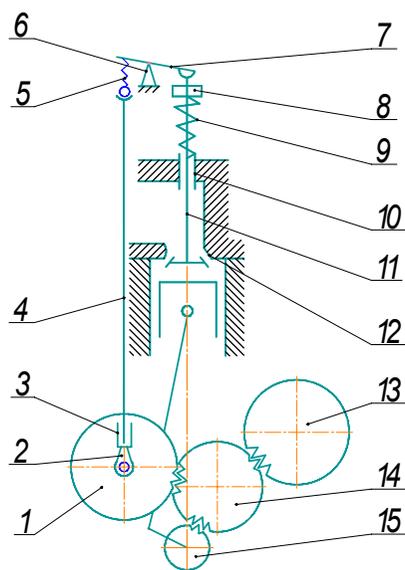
Схема газораспределительного и кривошипно-шатунного механизма двигателя Д-260:
